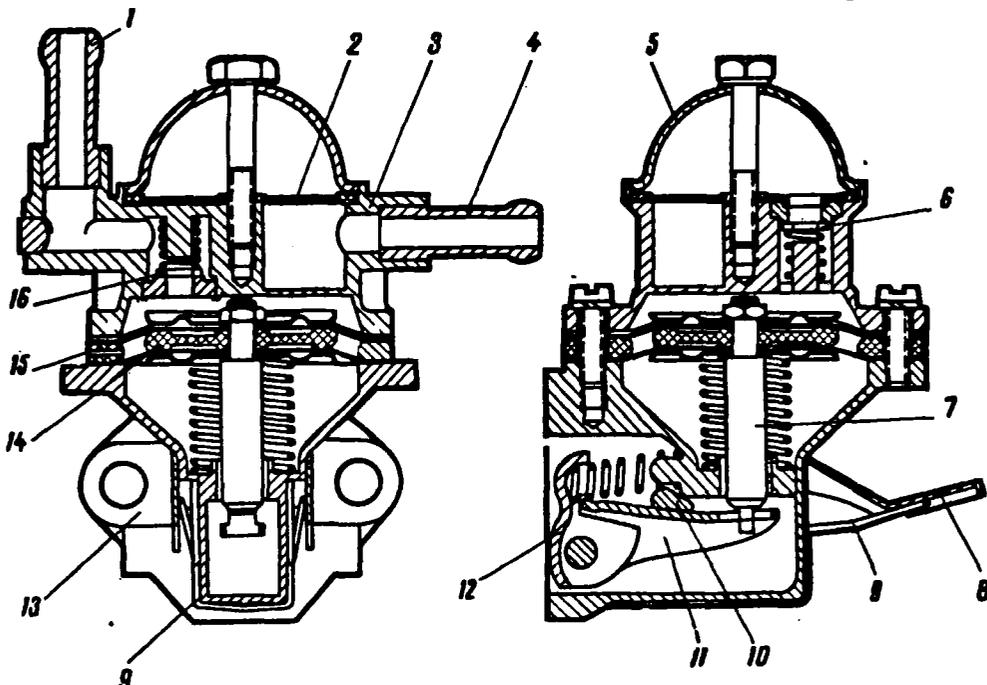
Топливный насос: 1 - нагнетательный патрубок; 2 - фильтр; 3 - корпус; 4 - всасывающий патрубок; 5 - крышка; 6 - всасывающий клапан; 7 - тяга; 8 - рычаг ручной подкачки; 9 - пружина; 10 - эксцентрик; 11 - баланси́р; 12 - рычаг механической подкачки; 13 - нижняя крышка; 14 - внутренняя дистанционная прокладка; 15 - наружная дистанционная прокладка; 16 - нагнетательный клапан
